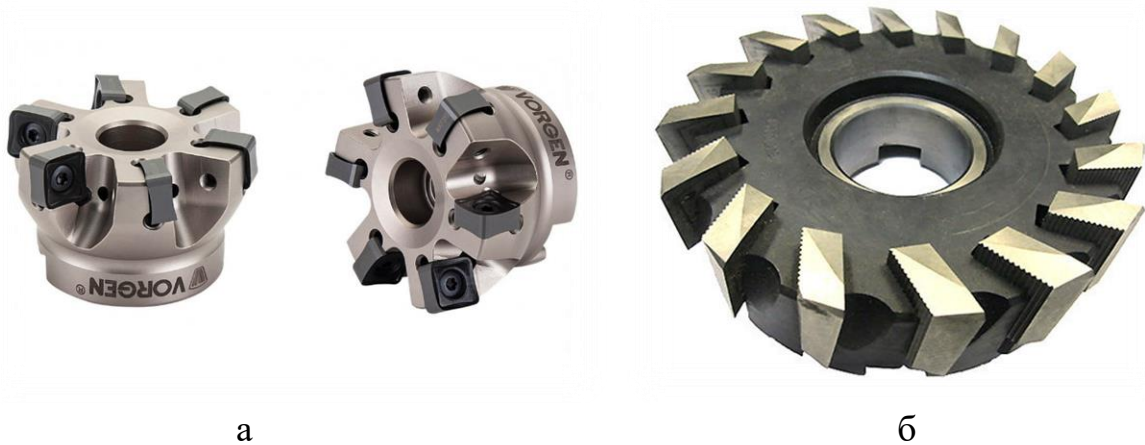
Приклади фрези: а - з твердосплавними пластинами;
